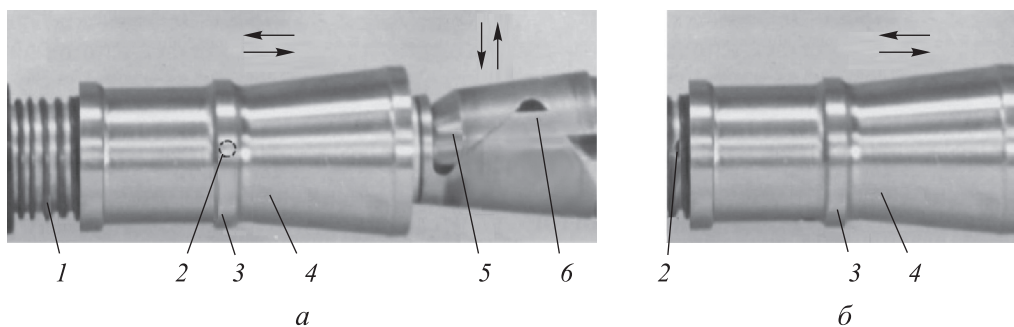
Внешний вид безазорного стыковочного устройства в исходном (а) и рабочем (б) положениях
